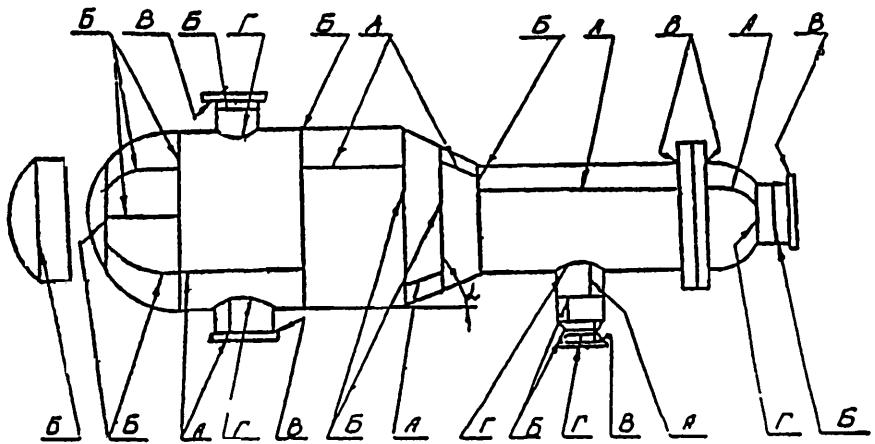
Расположение типовых сварных соединений и сборочных единиц А, Б, В, Г
